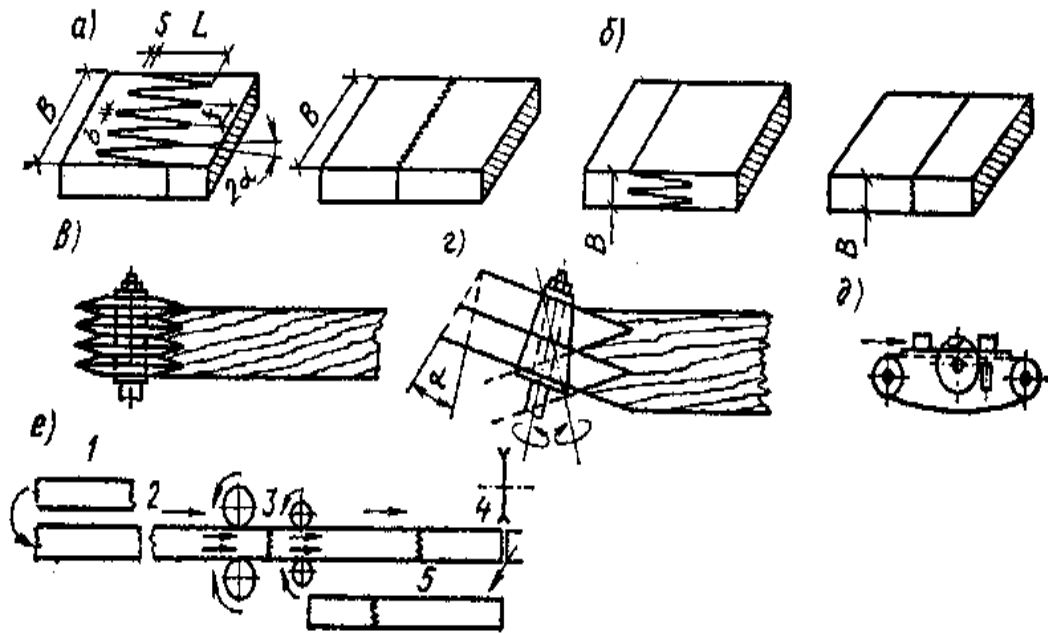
Торцеві наросчування, схеми фрезерування при торцевому склеюванні заготовок: *а* - вертикальне (по ширині деталі), зубчасте (клиновидне) з'єднання; *б* - горизонтальне (по товщині деталі), зубчасте (клиновидное) з'єднання; *в* - фрезерування зубчастого з'єднання; *г* - випилювання зубчастого з'єднання; *д* - фрезерування зубчастого з'єднання; *е* - з'єднання в торець і склеювання
